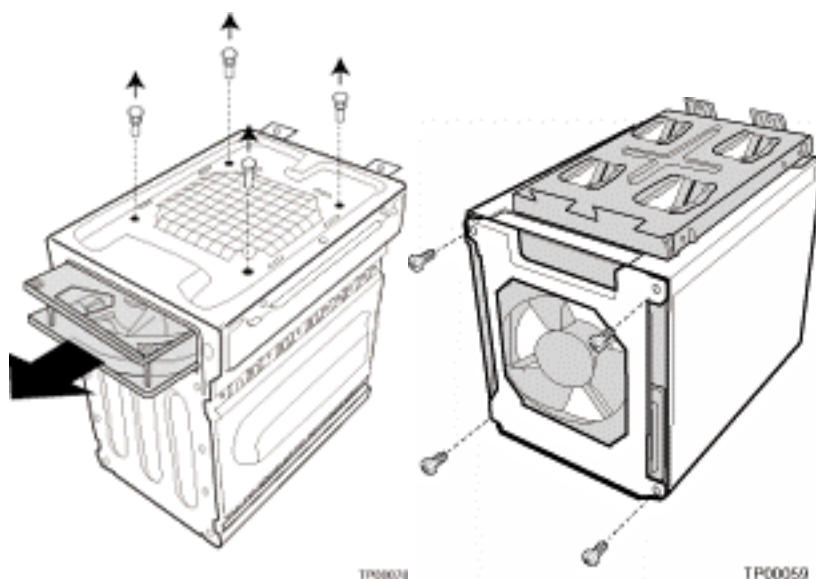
Перестановка вентилятора корпуса с салазок для жесткого диска IDE на салазки для жесткого диска SCSI
